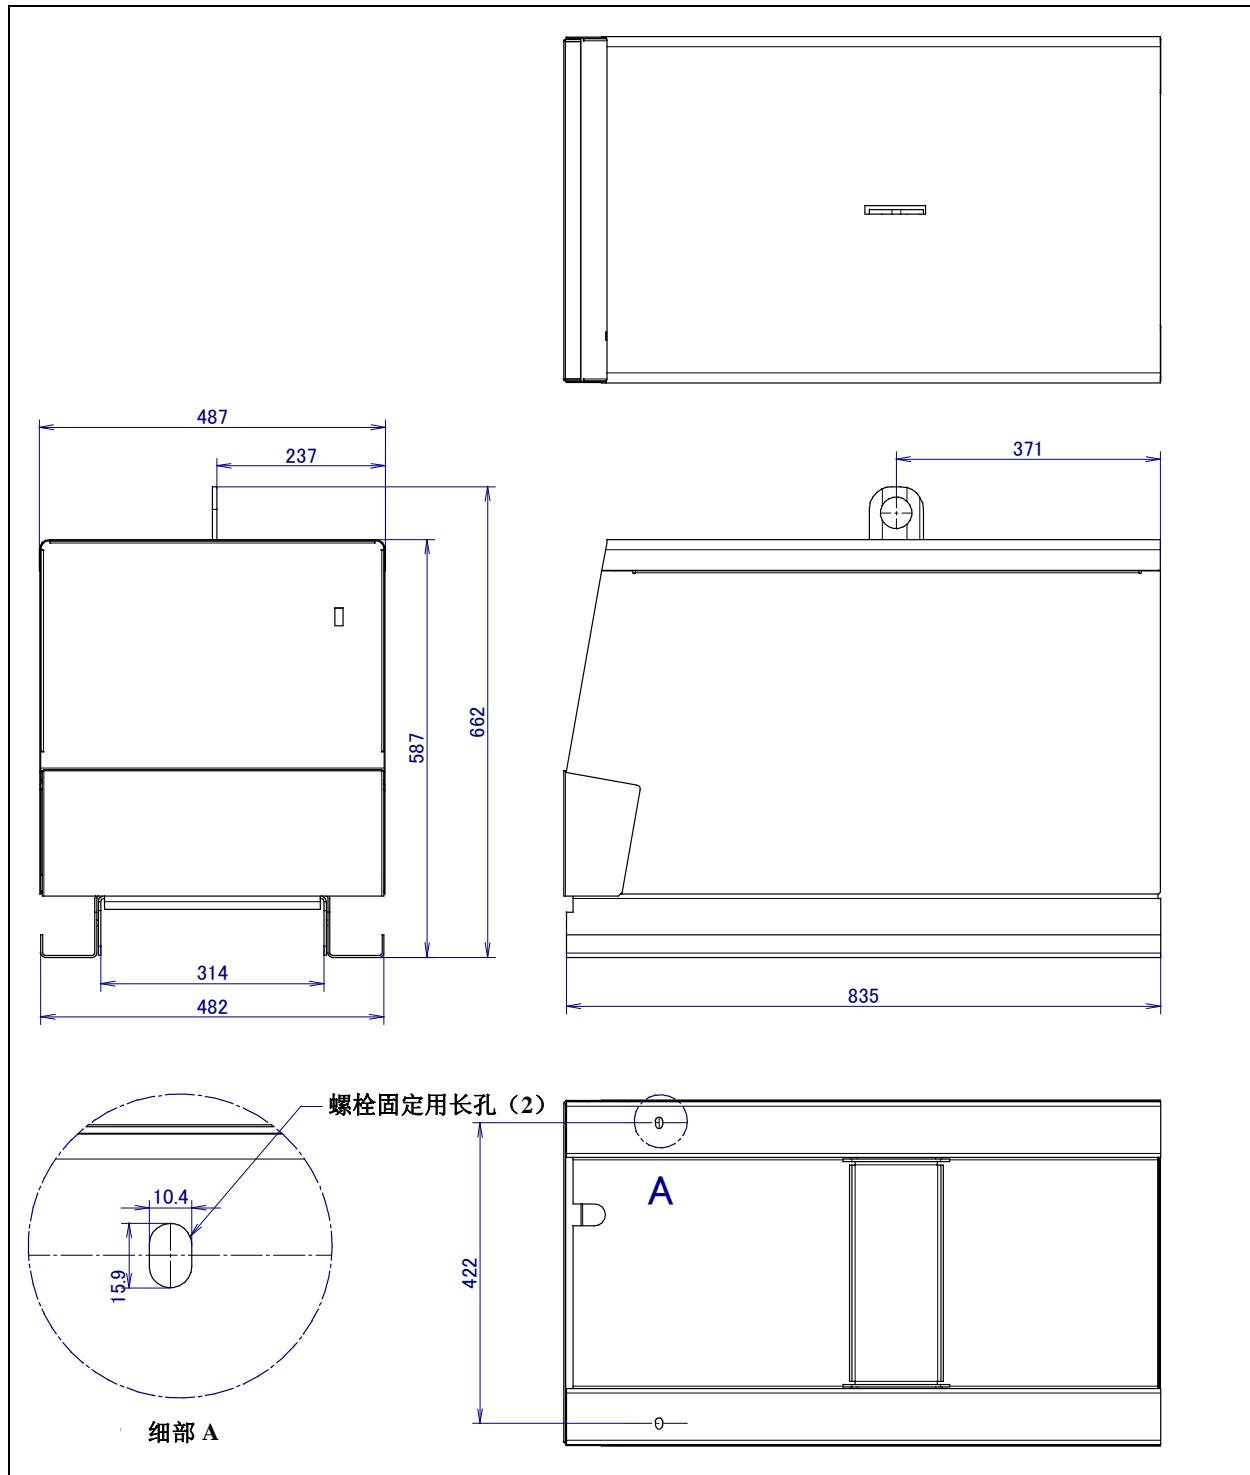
(b) ROBOWELD iC/H2 用焊接电源 (Power Wave 455M/STT)
